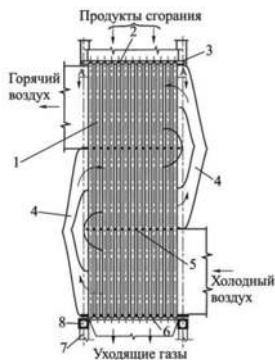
Трубчатый воздухоподогреватель. 1 - стальные трубы; 2, 6 - верхняя и нижняя трубные доски; 3 - компенсатор тепловых расширений; 4 - воздухоперепускной короб; 5 - промежуточная трубная доска; 7, 8 - опорные рама и колонны
